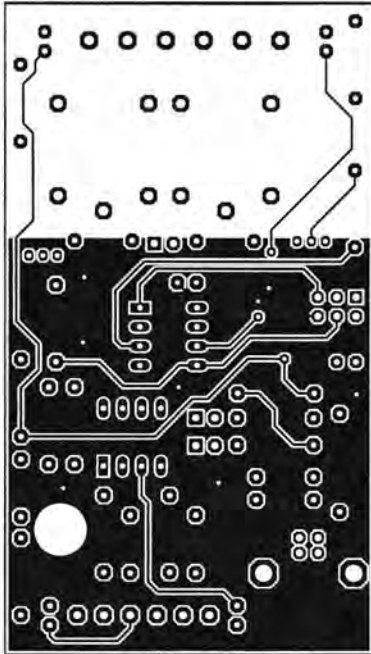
Layout der Platinoberseite; Abmessungen 49,3 mm × 86,3 mm, M 1:1
